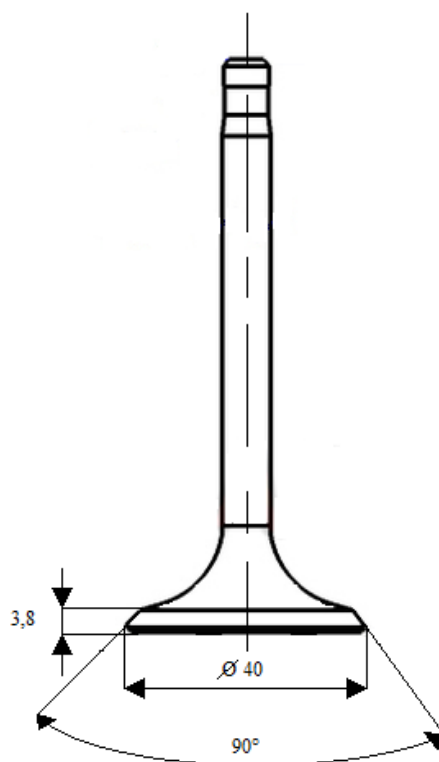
Obróbka ścierna talerzyka zaworu
